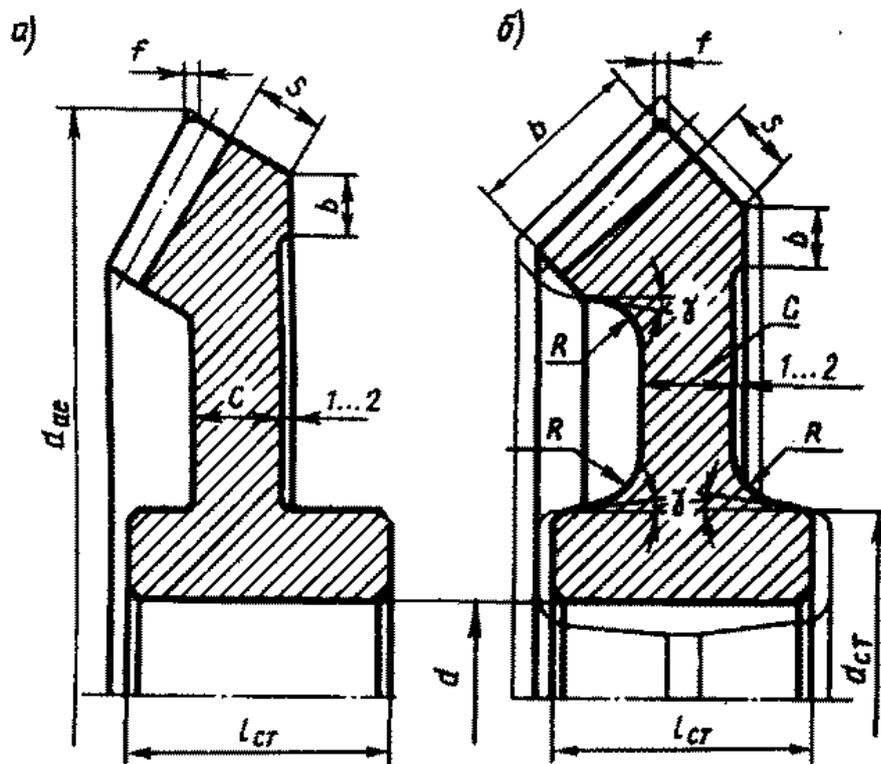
Конструктивные формы конических зубчатых колес с внешним диаметром вершин зубьев $d_{ae} > 120$ мм.
